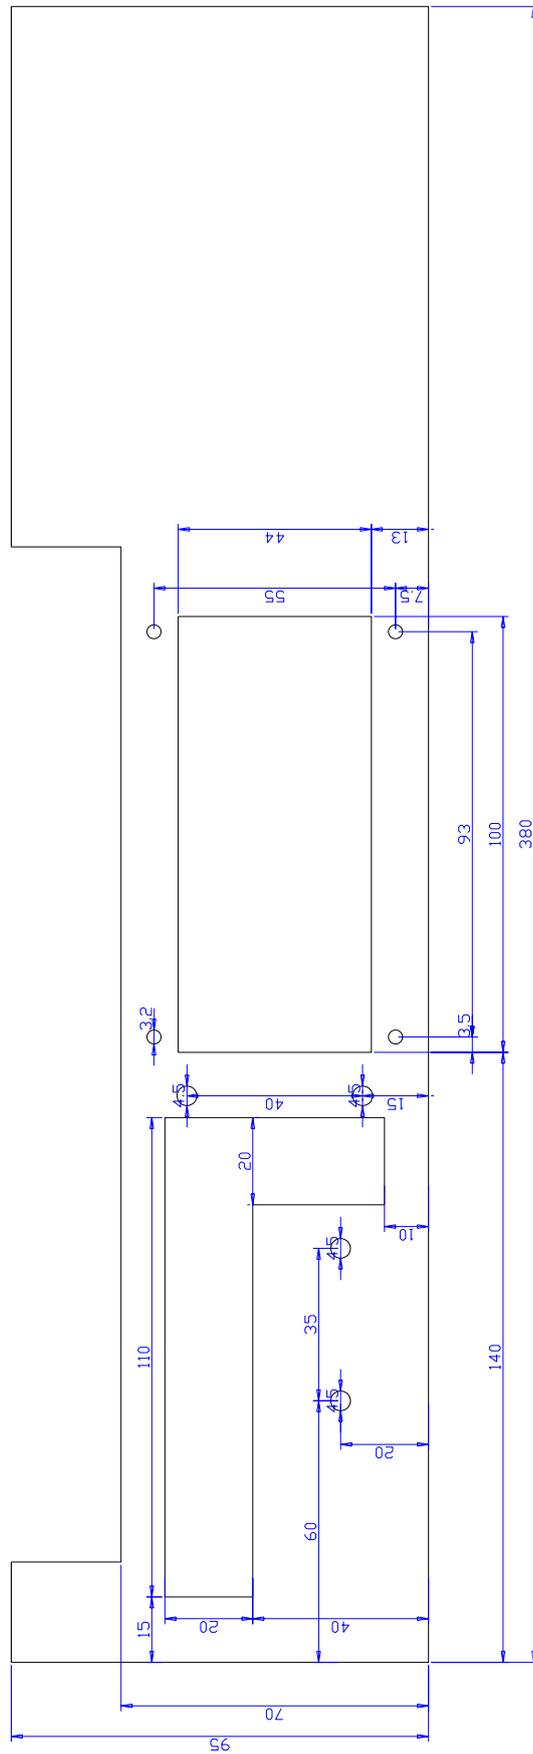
Technische Zeichnung der Frontplatte M 1:2
